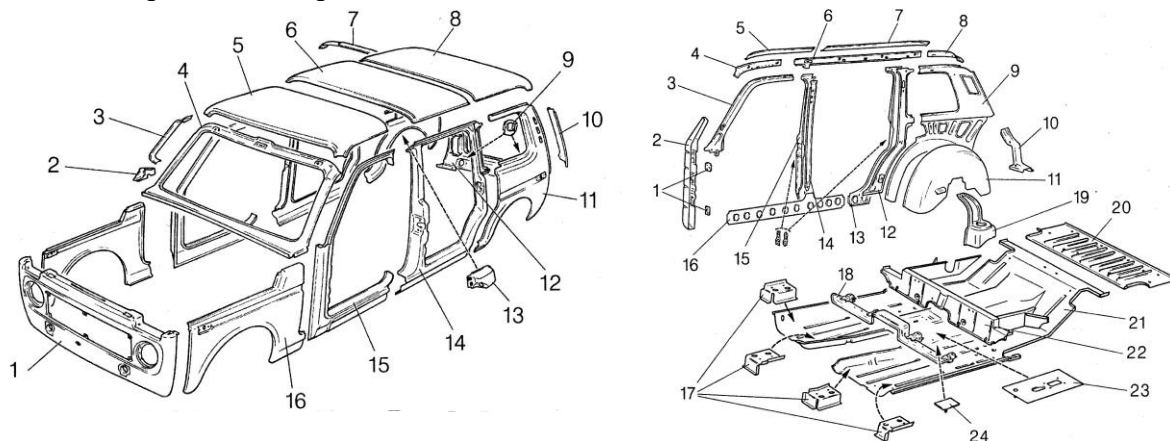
Элементы конструкции несущего кузова ВАЗ-2131.
